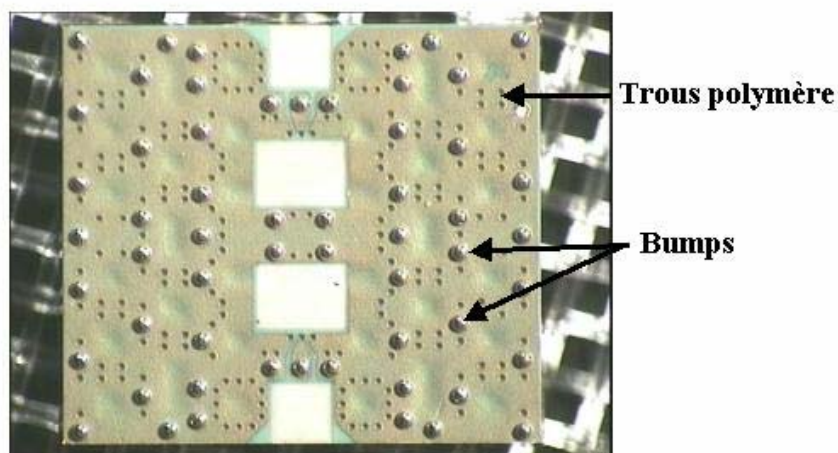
(a) Photographie du filtre silicium fabriqué avant le laminage du polymère
